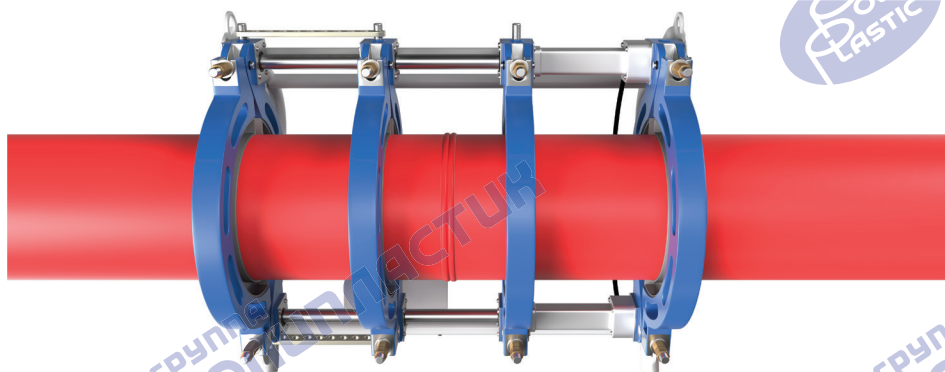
Сварка трубы нагретым инструментом встык
